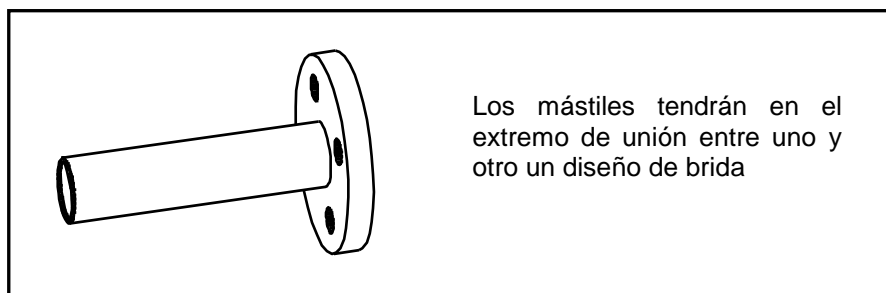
Extremo para unión entre los mástiles visto en planta
